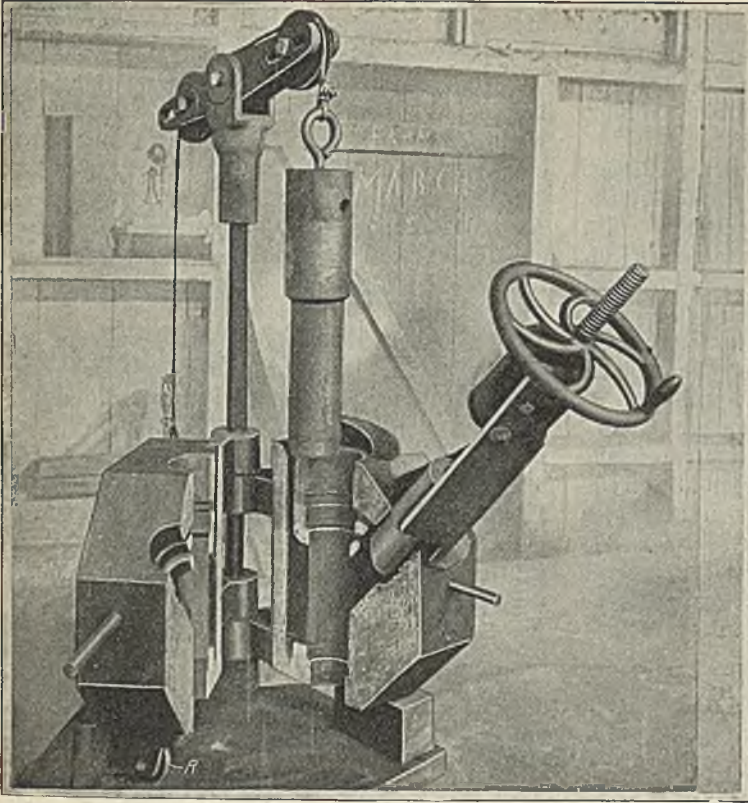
Formmaschine mit Vorrichtung zum Ausziehen der Kerne mittels Schrauben.
